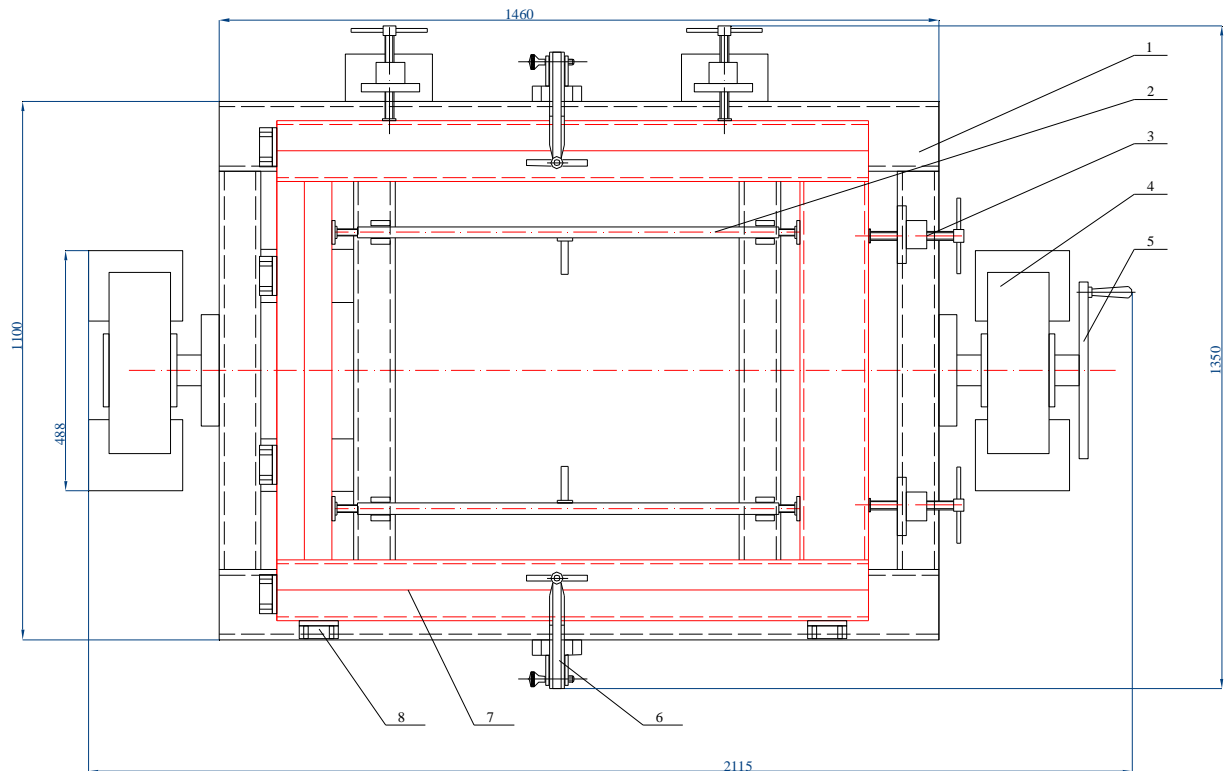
Сборочный кондуктор для сборки граней колонны.
